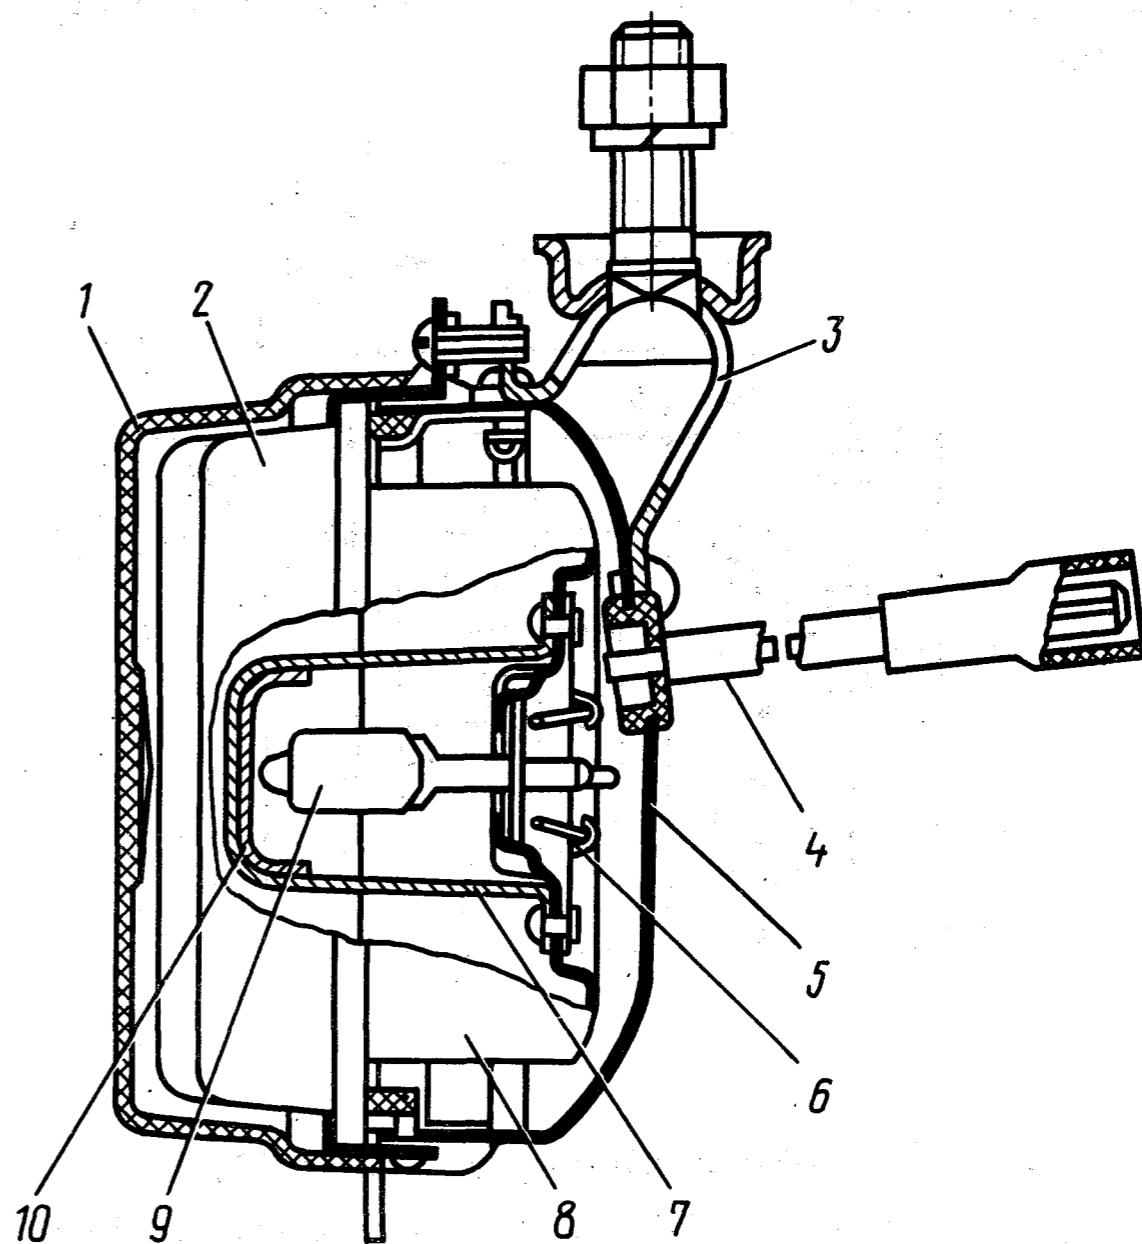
Фара противотуманная: 1 - крышка защитная; 2 - рассеиватель; 3 - кронштейн крепления; 4 - провод; 5 - корпус; 6 - держатель лампы пружинный; 7 - держатель экрана; 8 - отражатель; 9 - лампа; 10 - экран
